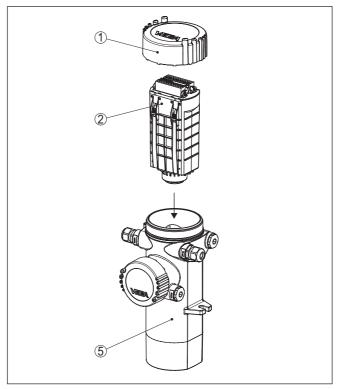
Elektronikeinsatz vorsichtig in das Gerätegehäuse einstecken
